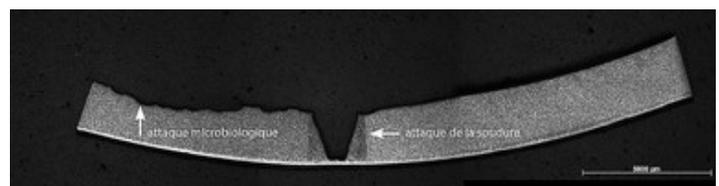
coupe métallographique de ce tube. Au milieu, on voit bien l'attaque préférentielle de la soudure. A gauche, on distingue également une attaque plus locale
